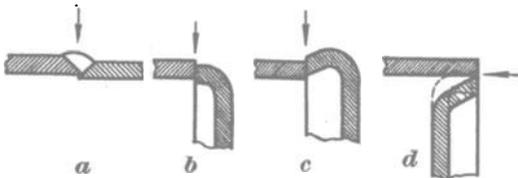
Falsche Schweißungen bei Blechböden.
